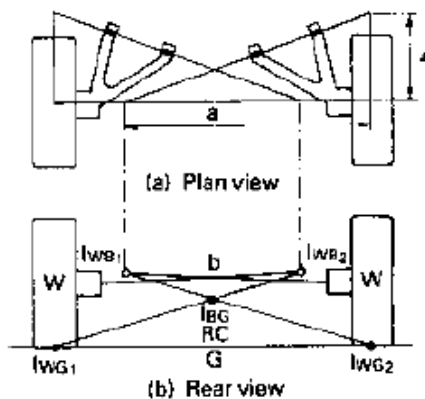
Esquema da suspensão *semi-trailing arm* e construção do centro de rolamento. [7]
